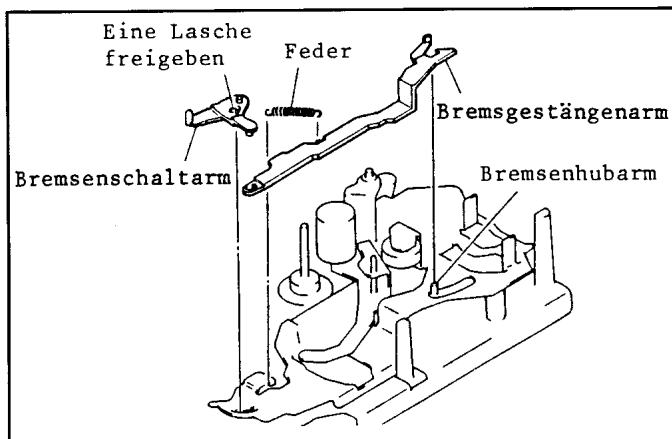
Bremsgestängearm, Bremsschaltarm
